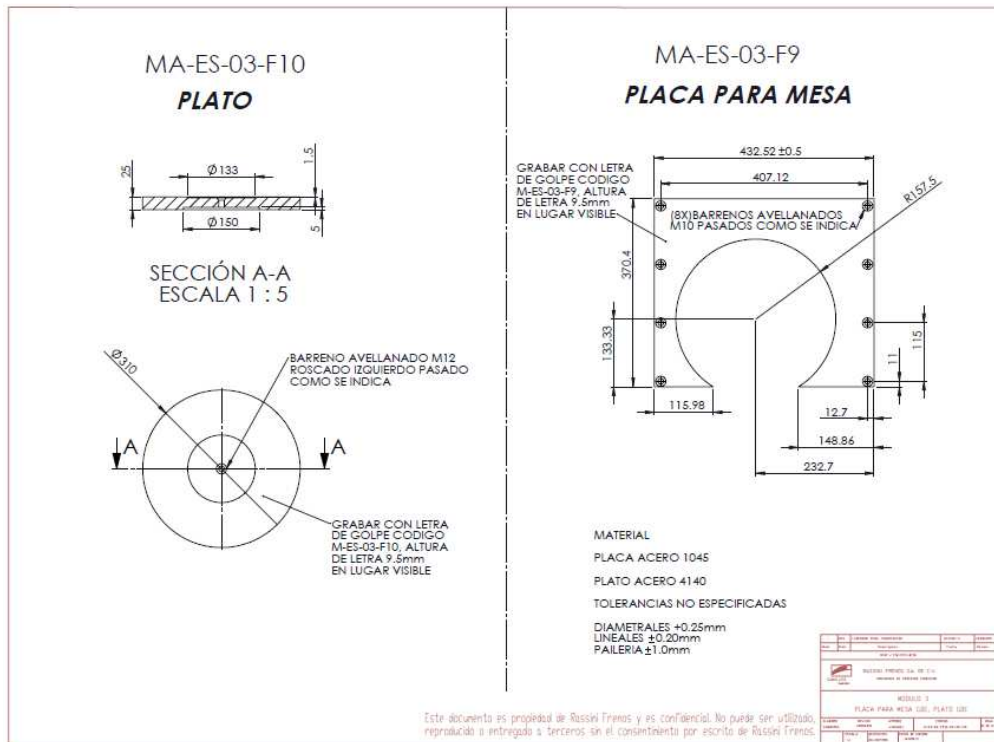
Plano de fabricación plato chico y placa para mesa
